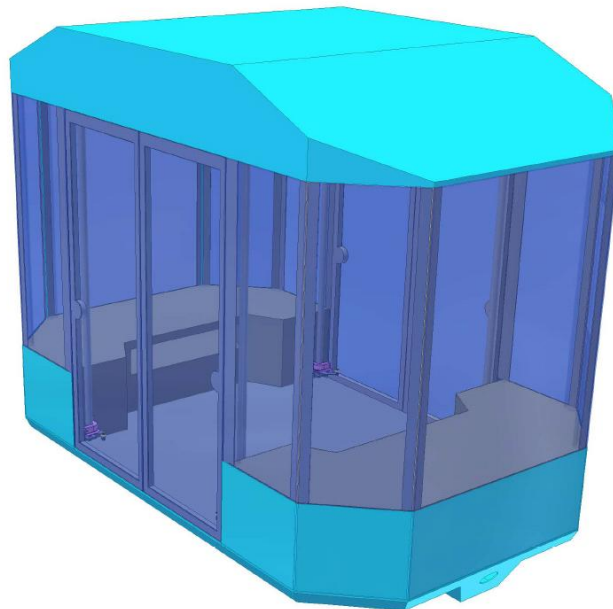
Корпус юнибуса Ю-324П исполнения 02
